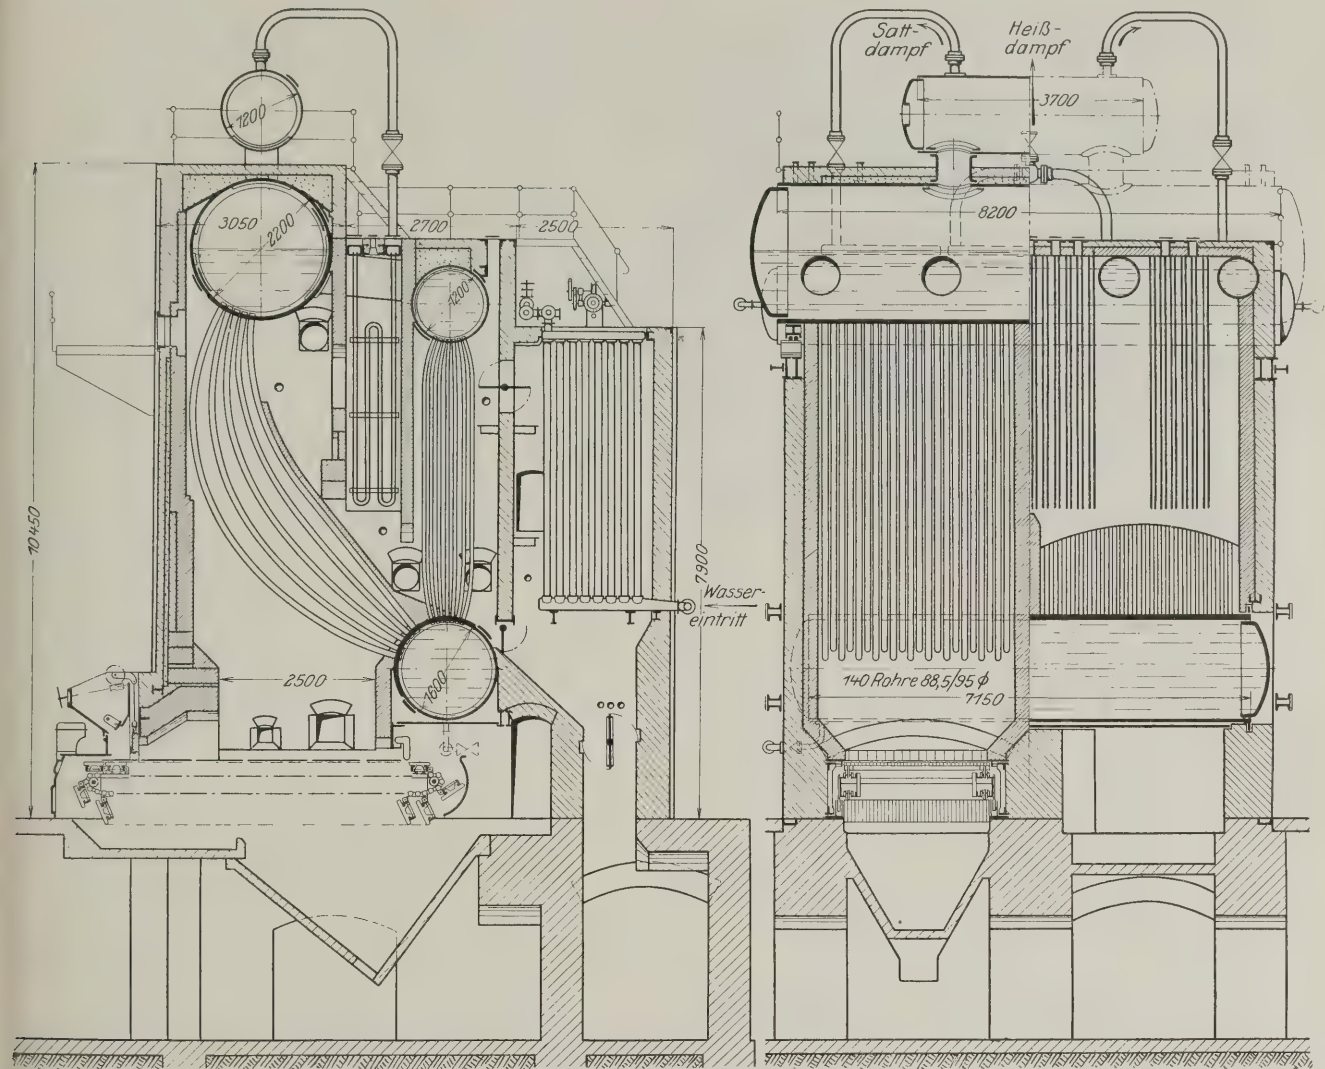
und 20. Dreitrommel-Steilrohrkessel. Bauart Dr. Otte, mit 600 m² Heizfläche für 15 at Betriebsdruck.
